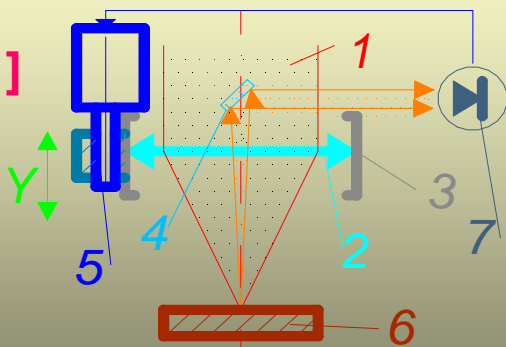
(10.10). Пристрій для позиціювання заготовки в горловину каустики пучка
